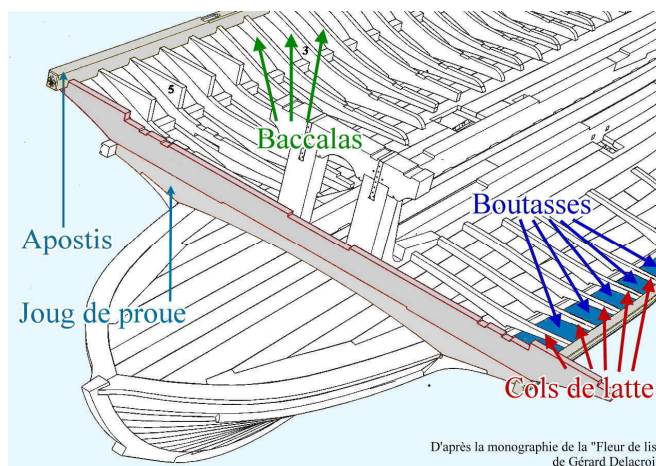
/02 – Cols de latte, boutasses et baccalas sur une galère française
